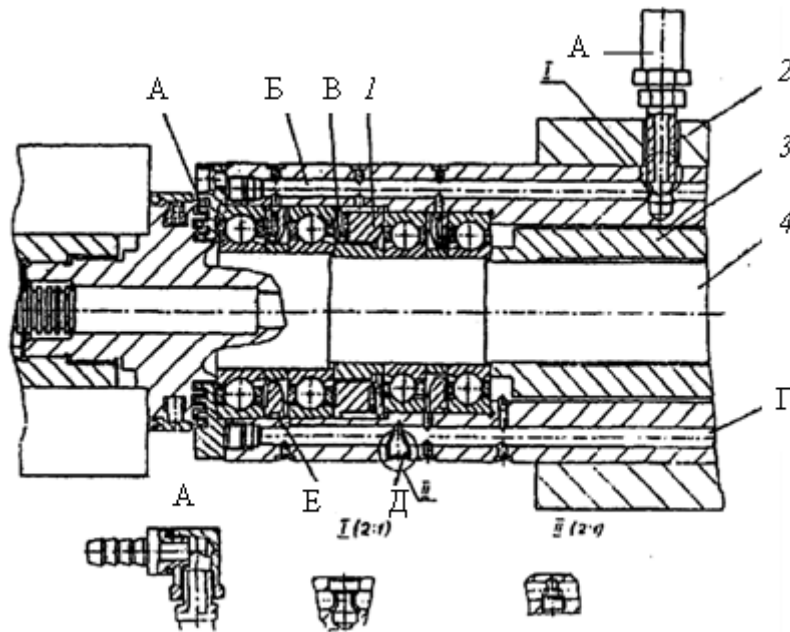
Передняя опора шпинделя внутришлифовального станка
